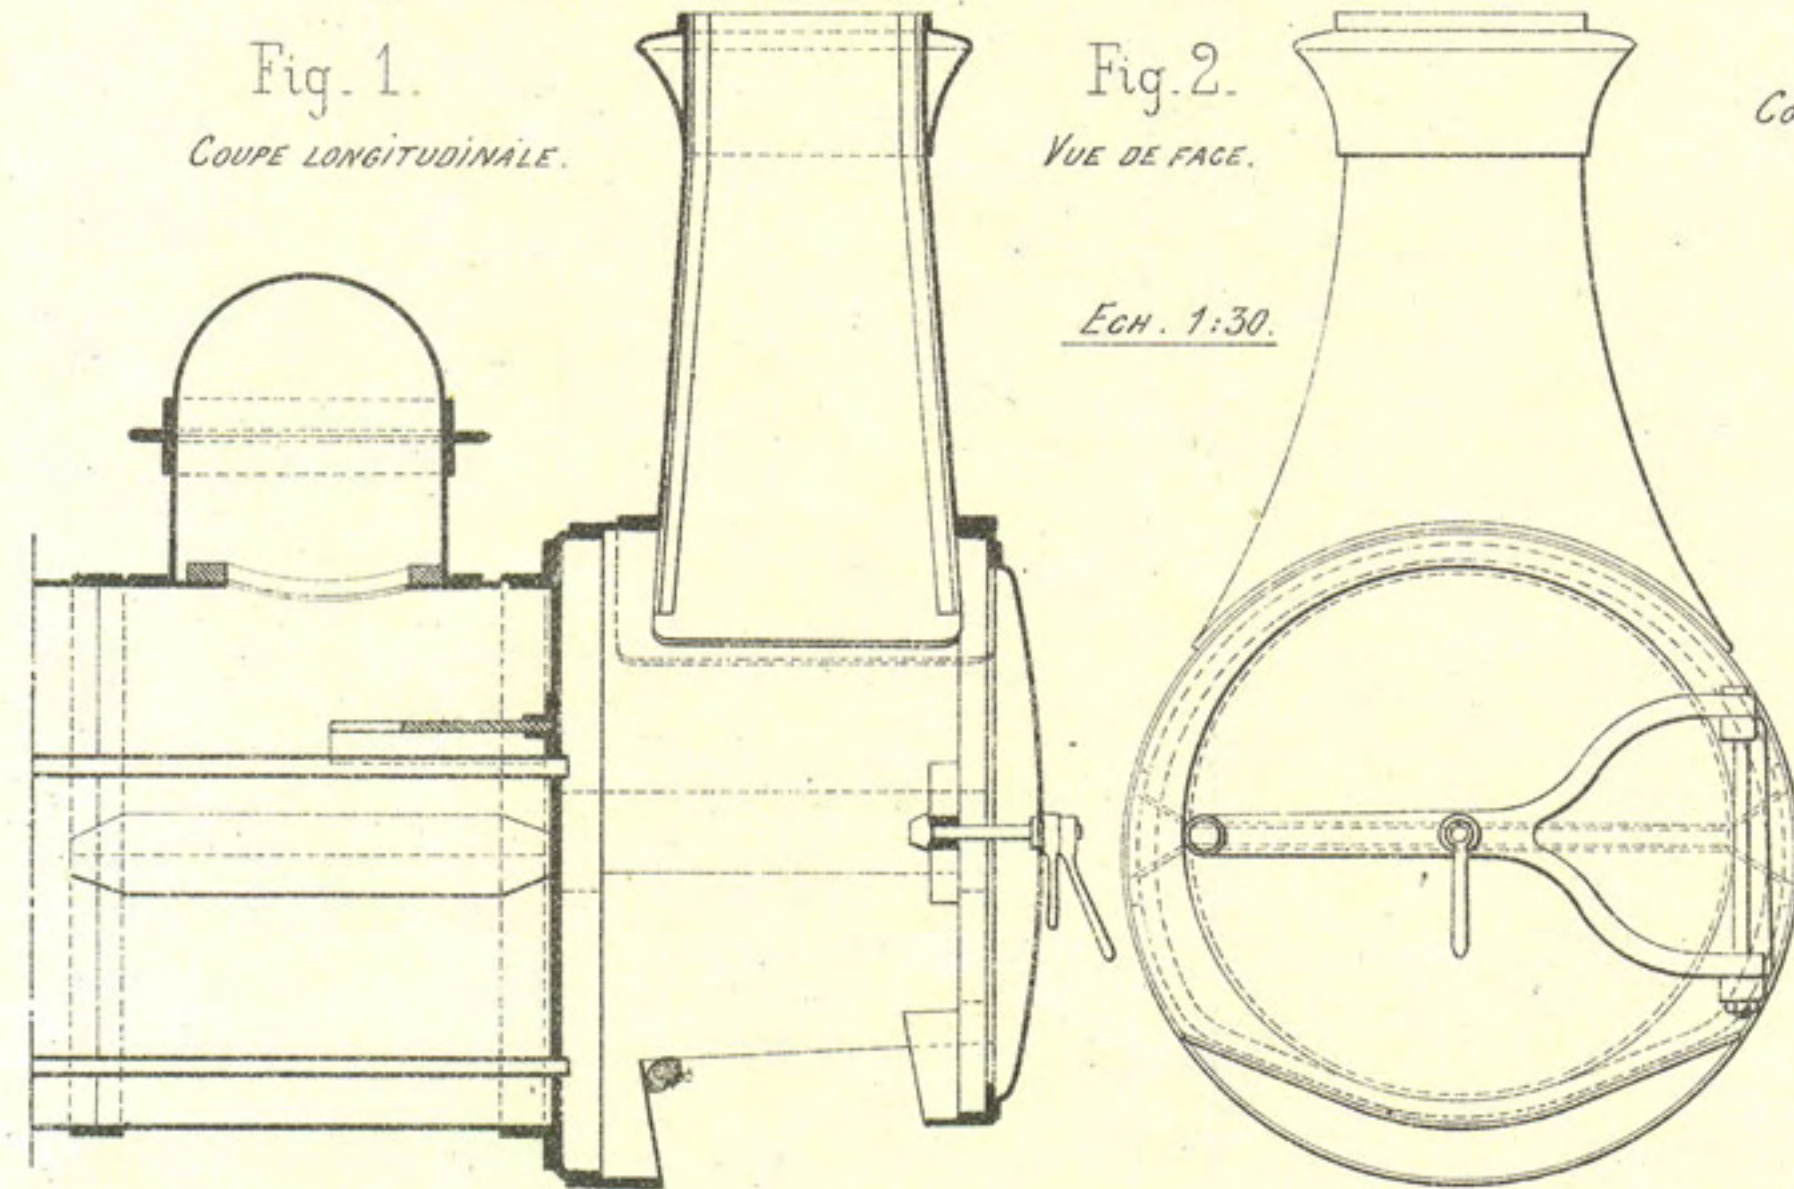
et 12. Corps cylindrique de divers types de machines Etat Belge.
